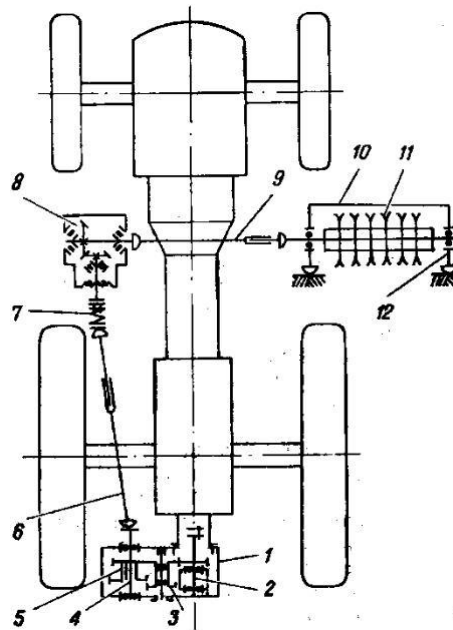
Фреза садова ФСН-0,9Г:
